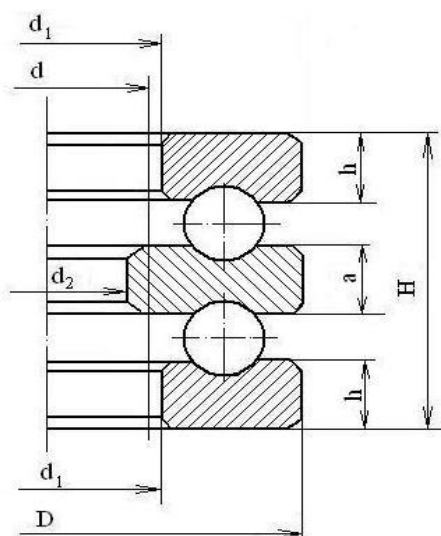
Подшипник шариковый упорный двухрядный
